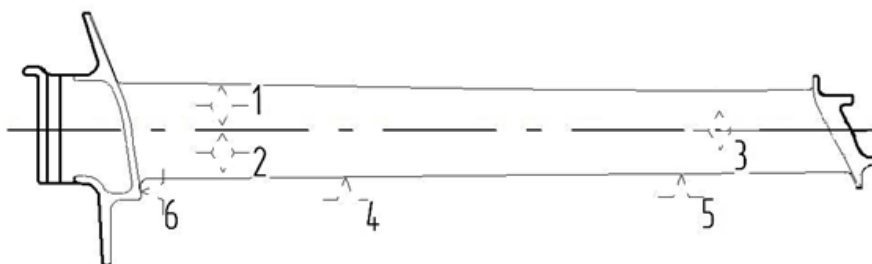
Базирование заготовки за проточную часть в приспособлении кассетного типа
